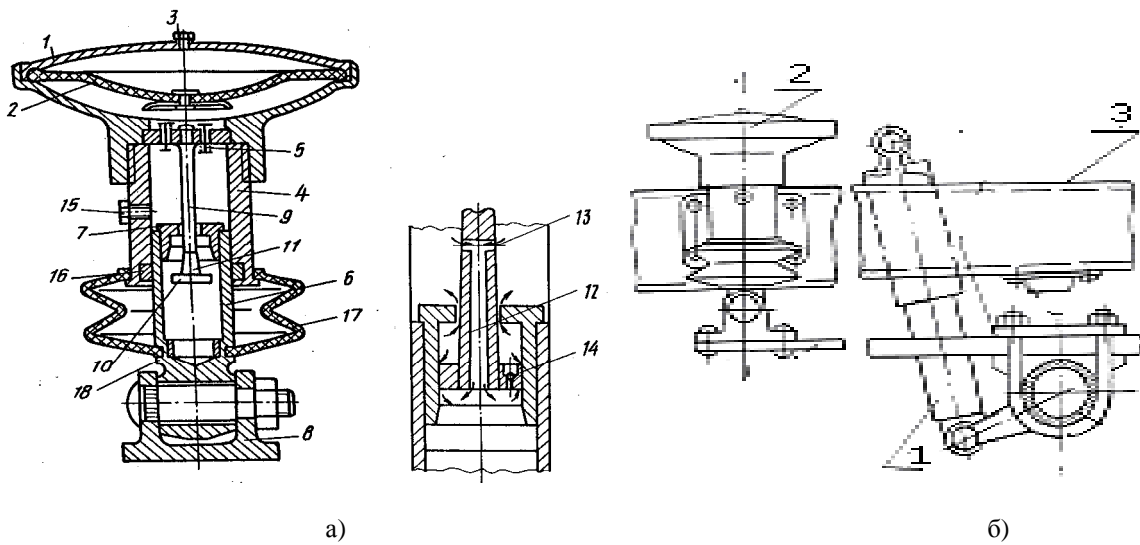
Схема гидропневматического упругого элемента подвески (а) и общий вид подвески (б): а) 1 - газовый баллон; 2 - разделительная диафрагма; 3 - газовый клапан; 4 - цилиндр; 5 - подпружиненный клапан; 6 - пружинный шток; 7 - гильза; 8 - шарнир; 9 - стержень; 10 - цилиндрическая головка; 11 - хвостовик; 12 - осевой канал; 13 - радиальный канал; 14 - обратный клапан; 15 - гидроштуцер; 16 - сегментные магниты; 17 - чехол; 18 - постоянный магнит; б) 1 – амортизатор; 2 - гидропневматический упругий элемент; 3 - рама
